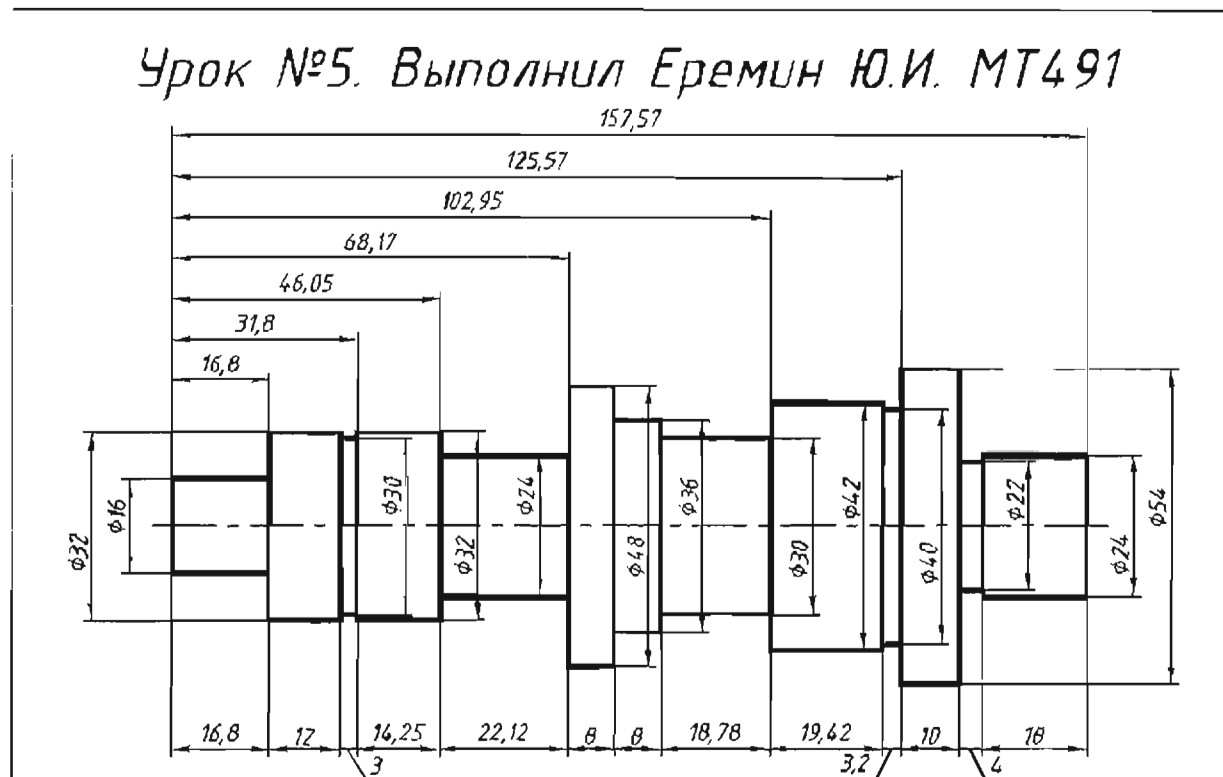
Чертеж вала с двумя вариантами простановки линейных размеров
